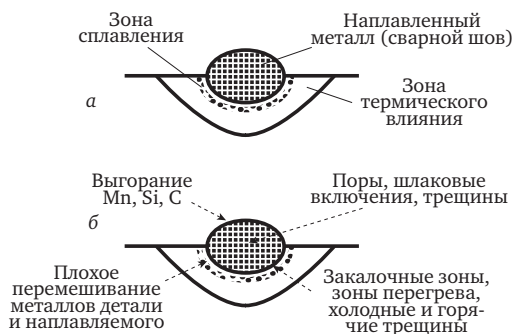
Зоны сварного шва (а) и возможные дефекты в нем (б)
